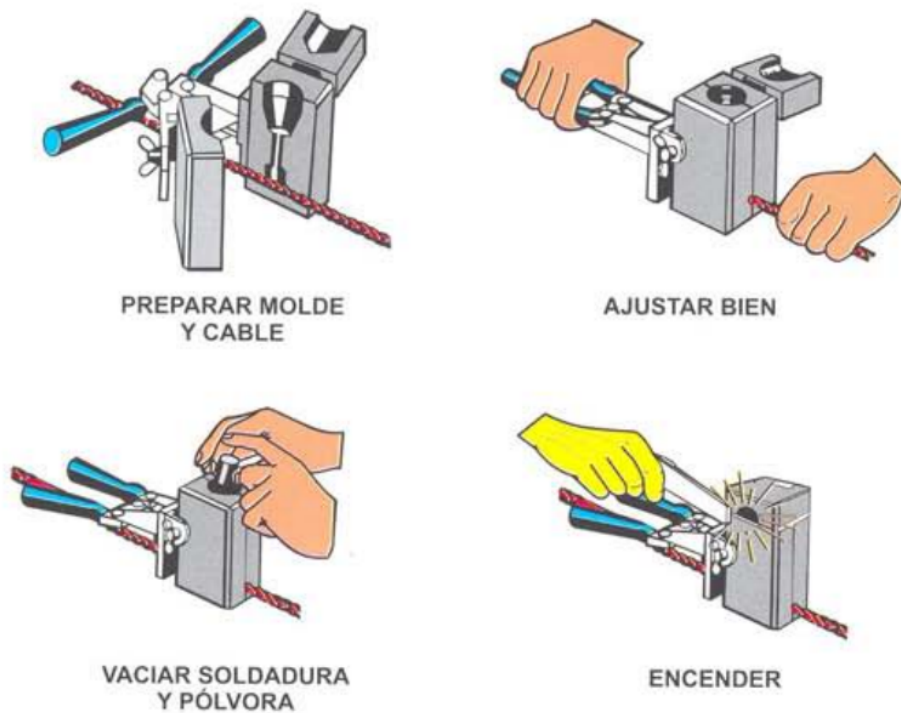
Proceso de aplicación de soldadura exotérmica [6].
